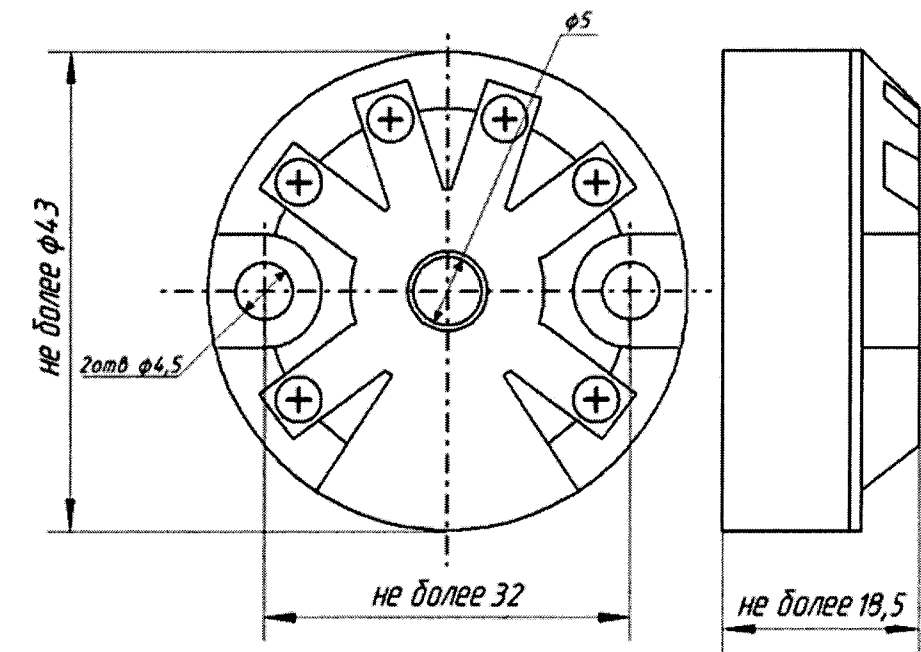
Корпус К для установки внутри клеммной головки ПП. Степень защиты IP20.
